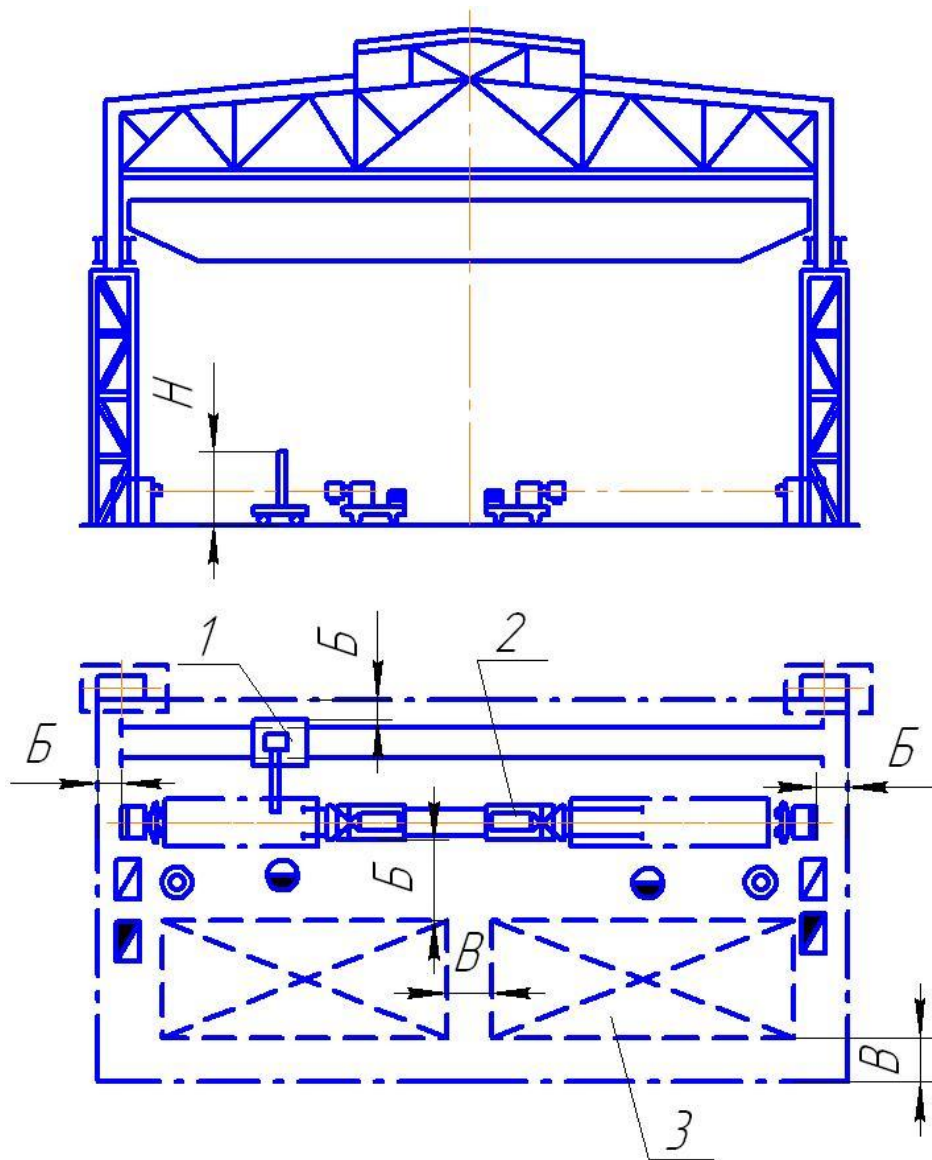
Размещение участка автоматической сварки с глагольной тележкой:
